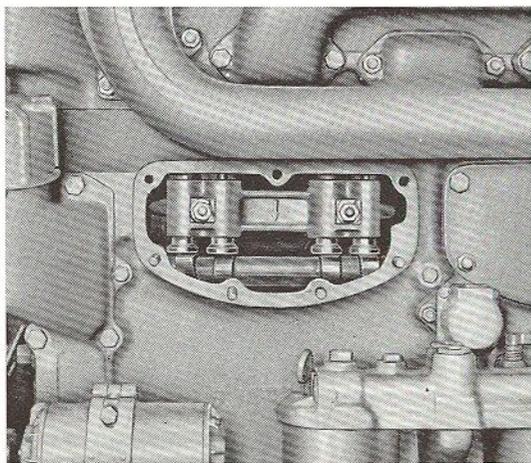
Accès aux poussoirs de commande des soupapes.
